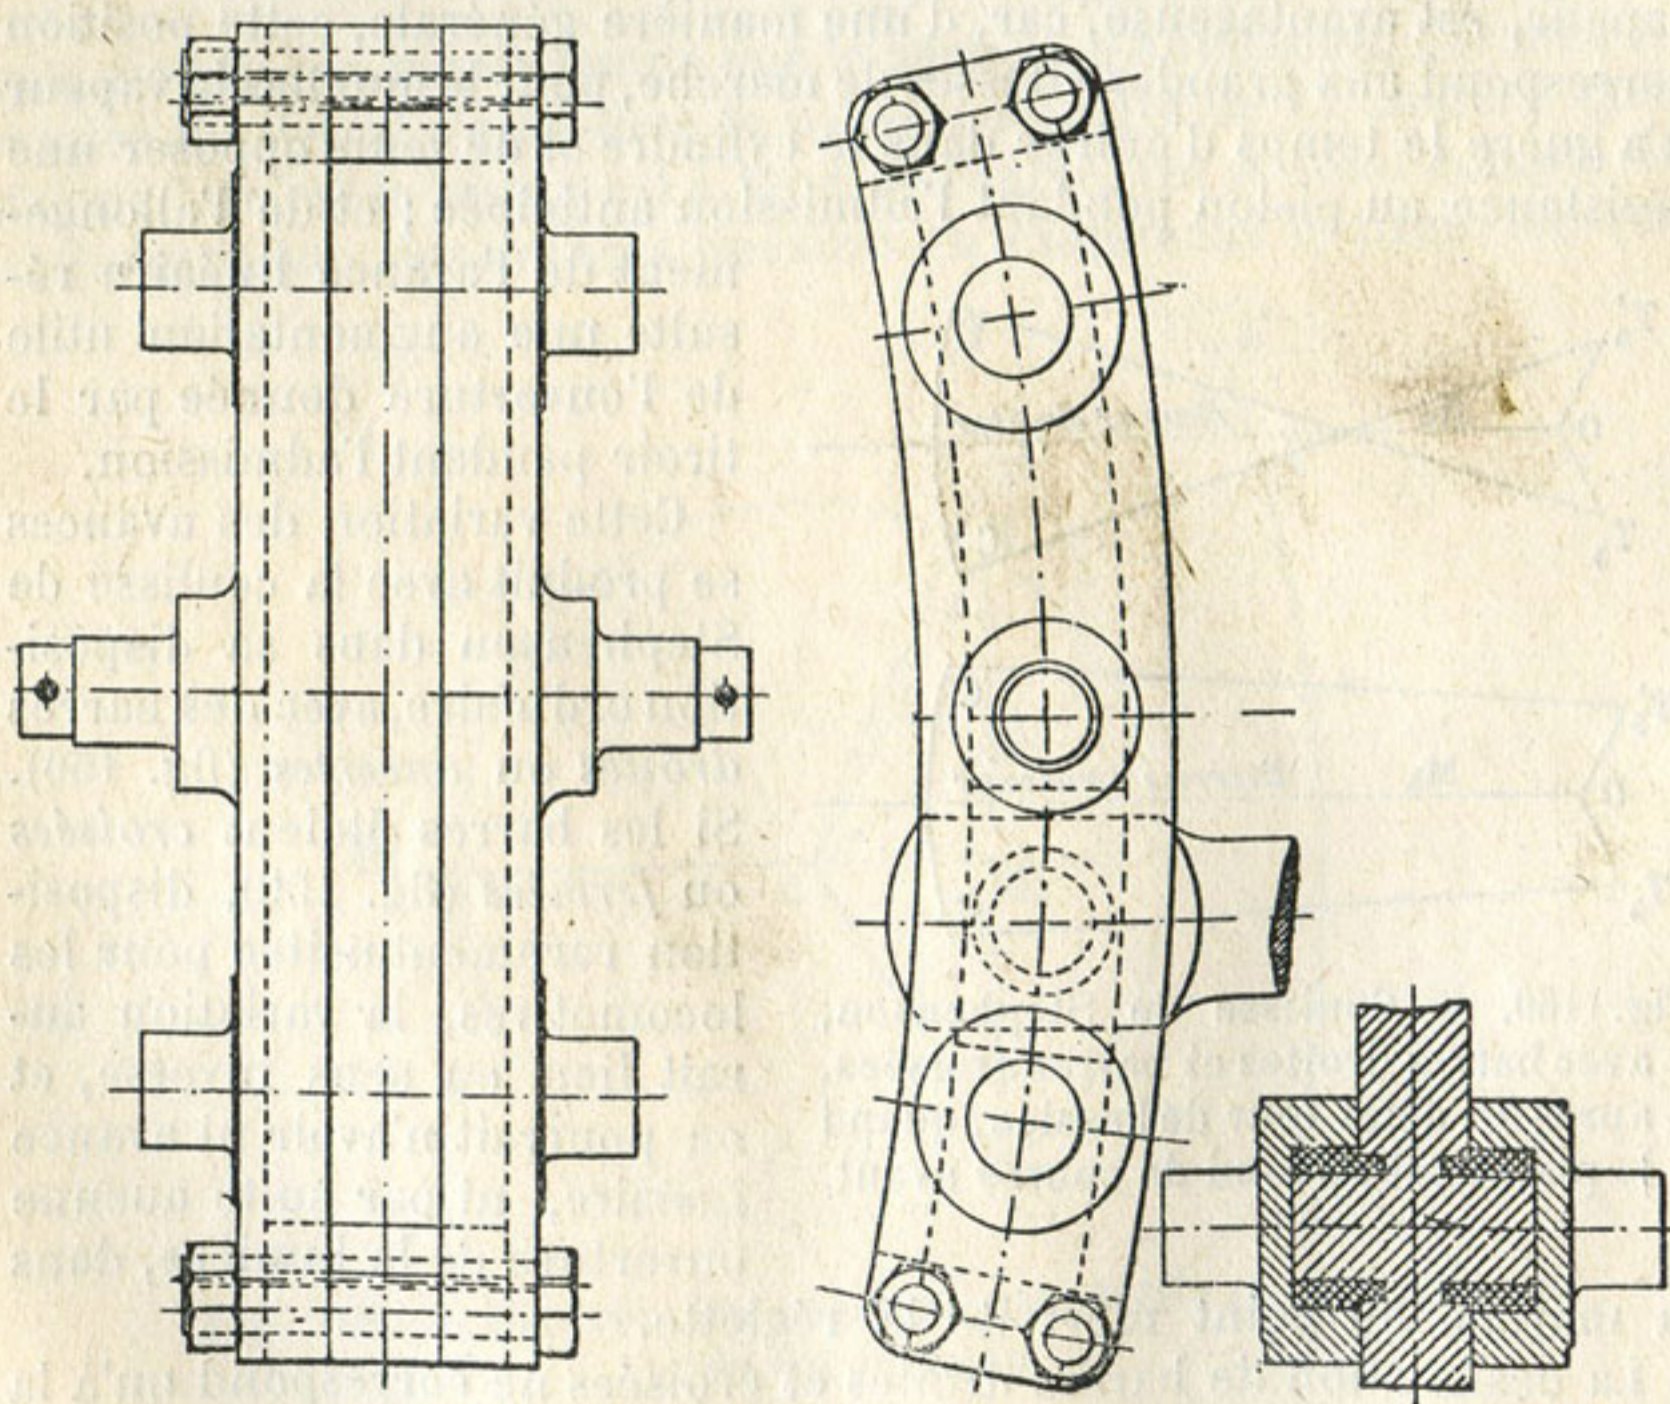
Coulisse de Stephenson à flasques ; élévations, transversale et longitudinale ; coupe par un plan horizontal.
